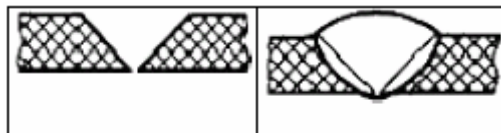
Схематичне зображення зварного з'єднання «С10»
